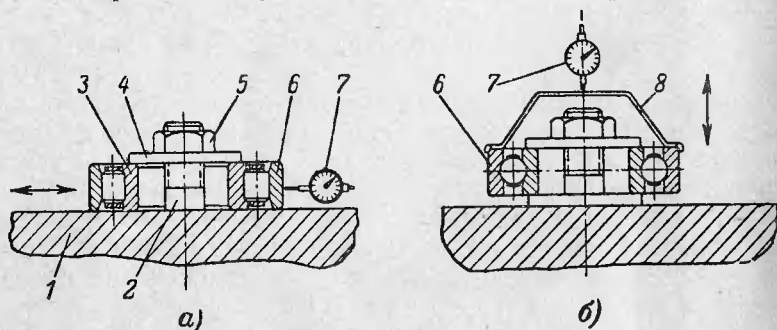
Замеры радиального зазора и осевой игры в подшипнике.
